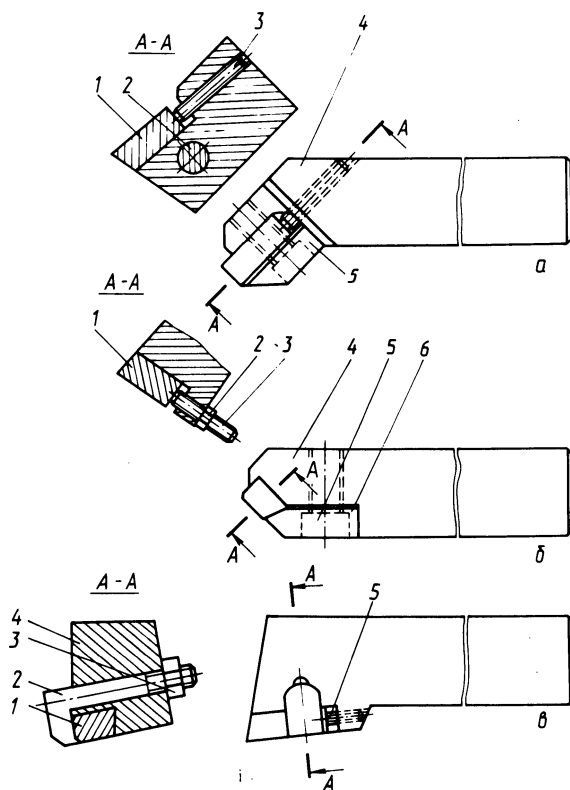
Сборный токарный резец: а – с расположением пластины опорой по большей грани и прихватом сбоку; б – с расположением пластины столбиком и прихватом сбоку; в – с расположением пластины с опорой по боковой стороне и Г-образным прихватом.
